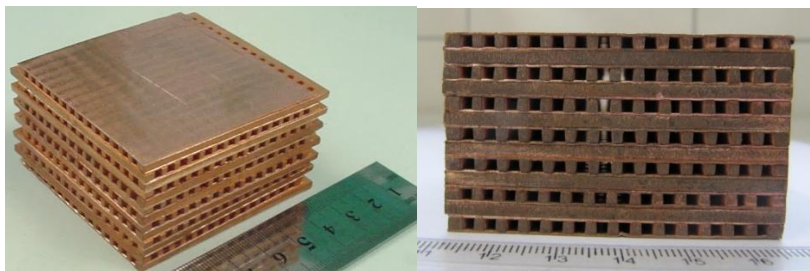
Núcleo produzido com a tecnologia de placa usinada antes e após o corte das laterais [6].
